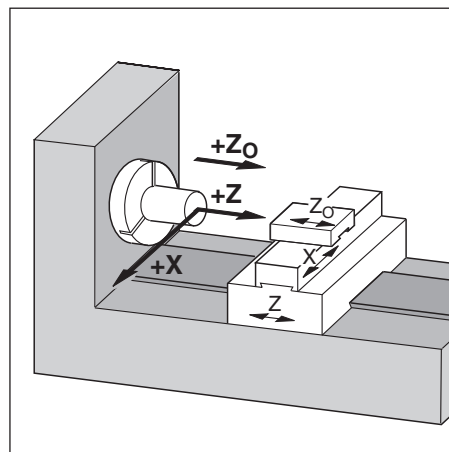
Kartézská souřadnicová soustava u soustruženého předmětu
